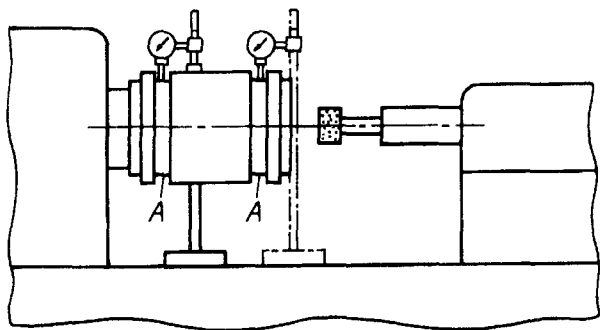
Схема приспособления, снабженного выточками для контроля его положения
